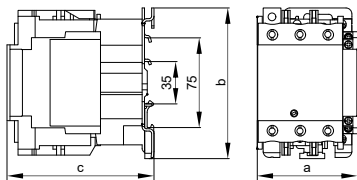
Габаритные размеры контакторов КМИ-А-46512–КМИ-А-49512 / Figure 4 — Overall dimensions of contactors KMI-A-46512–KMI-A-49512
